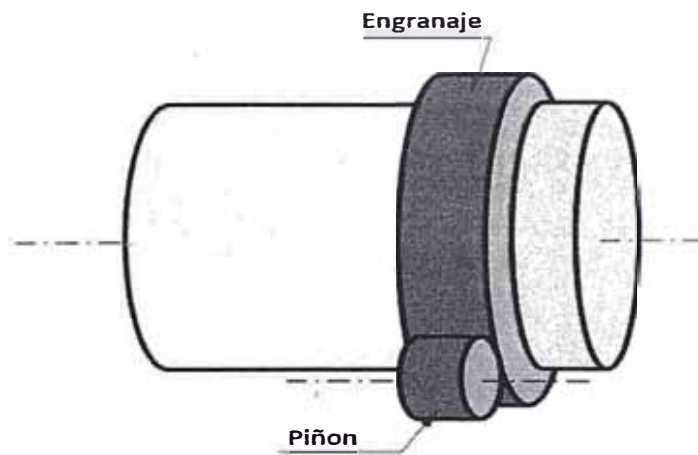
Esquema de tren de transmisión piñón – engranaje
